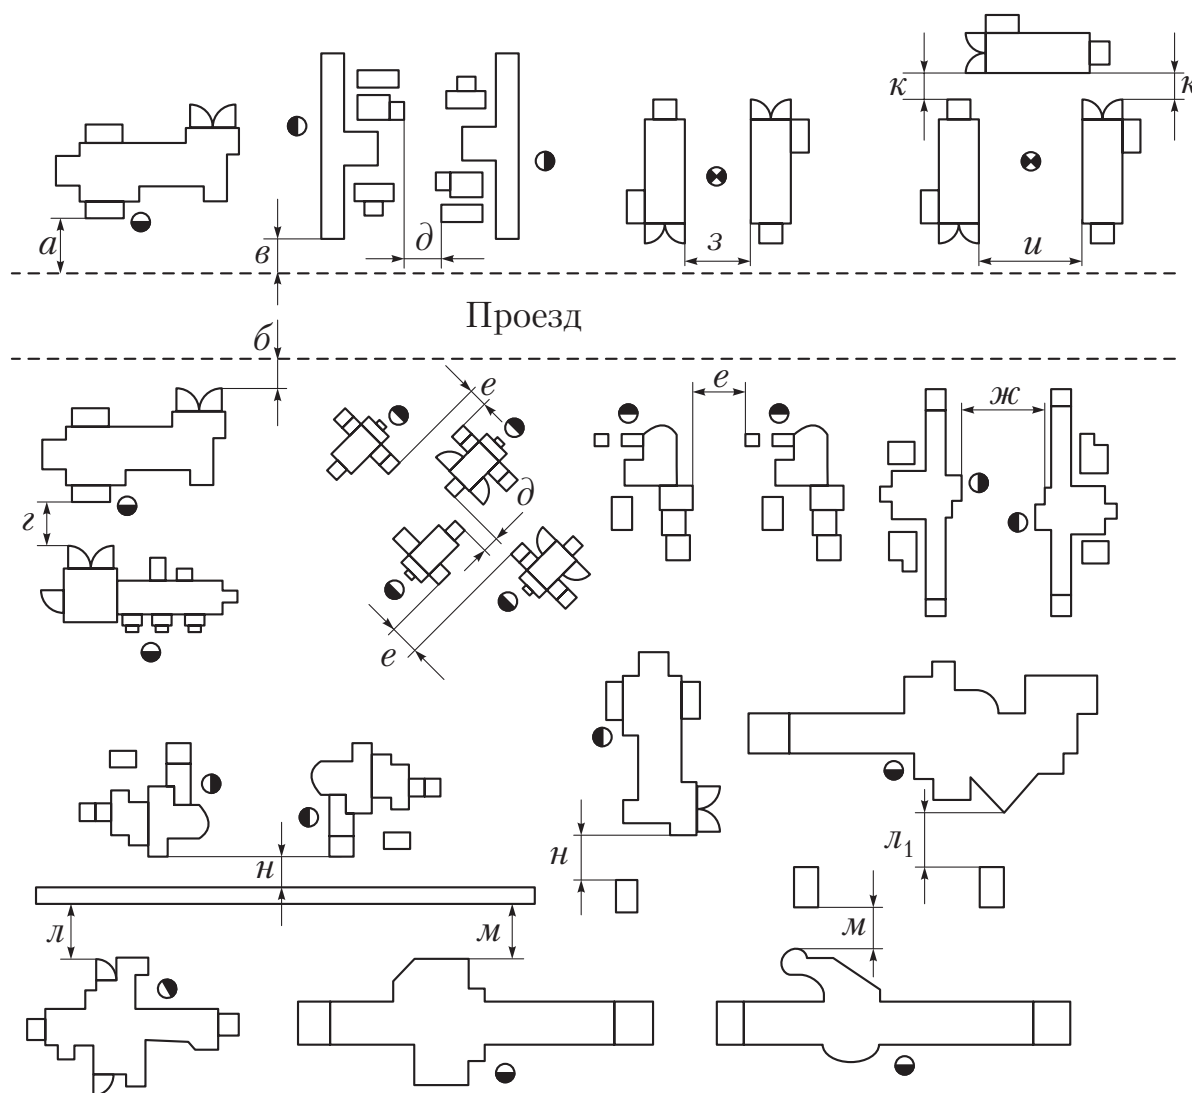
Варианты размещения станков относительно проездов, друг друга, стен и колонн здания
